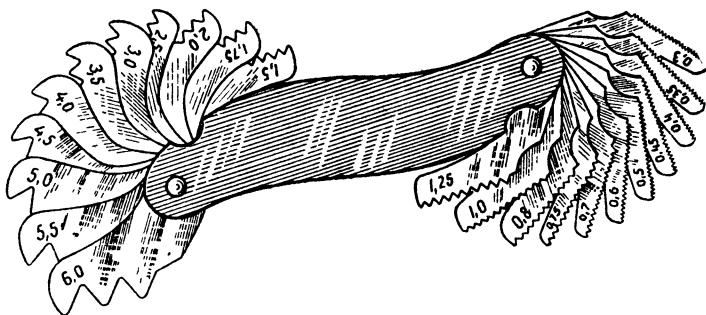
Резьбомер для проверки профиля резьбы и резьбового кольца.
